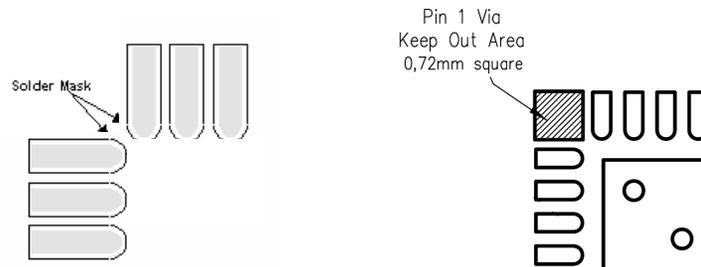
PCB 阻焊层和禁止区域示例
